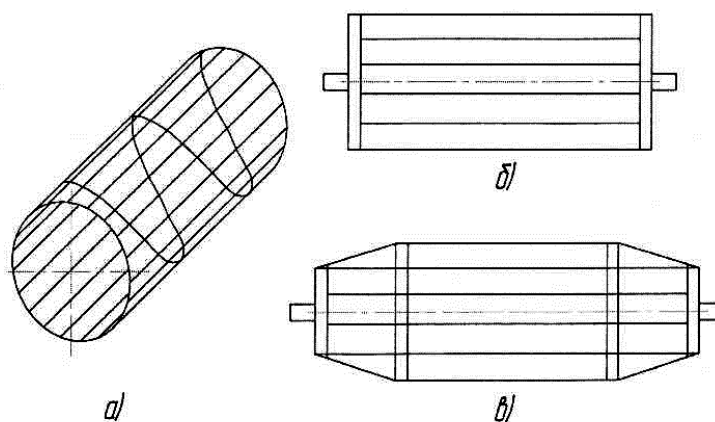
Барабанні конвеєри-очисники: а – загальний вигляд; б – циліндричний; в – складовий.
